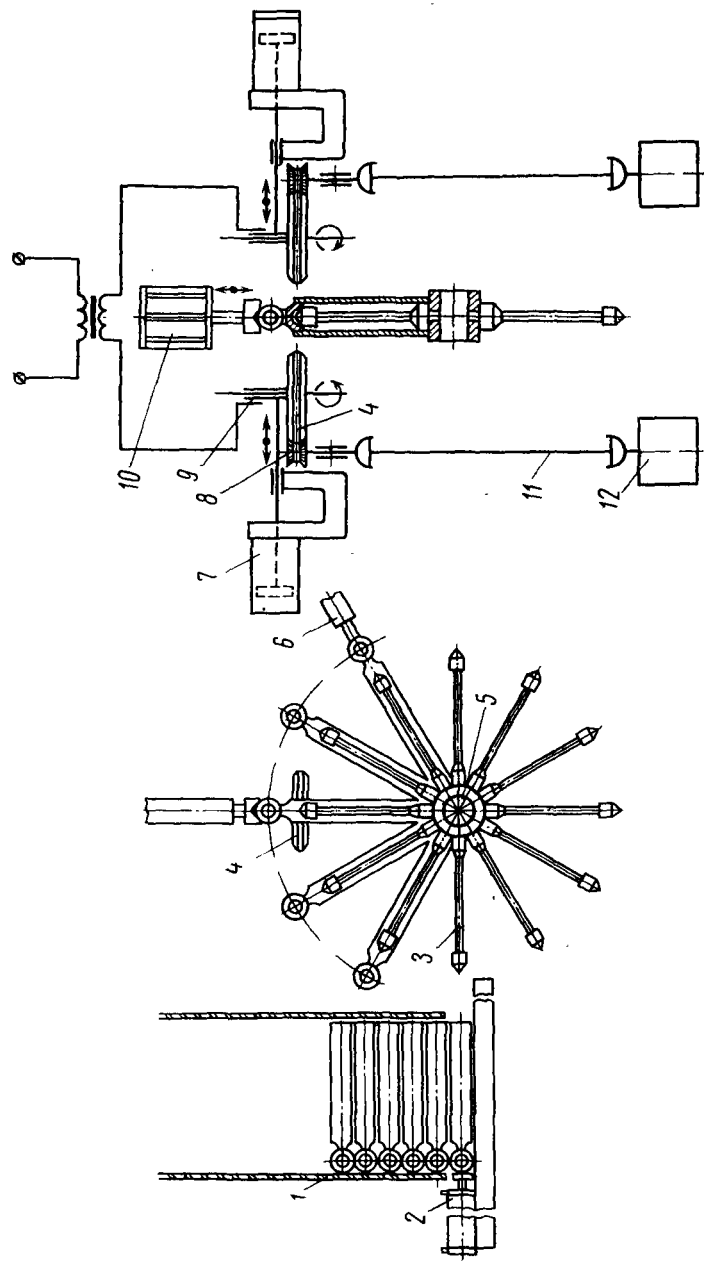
Принципиальная схема автомата для роликовой сварки узлов гидрооргтезаторов
